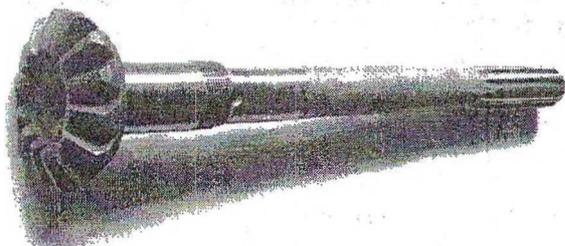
Вал-шестерня редуктора переднего ведущего моста
